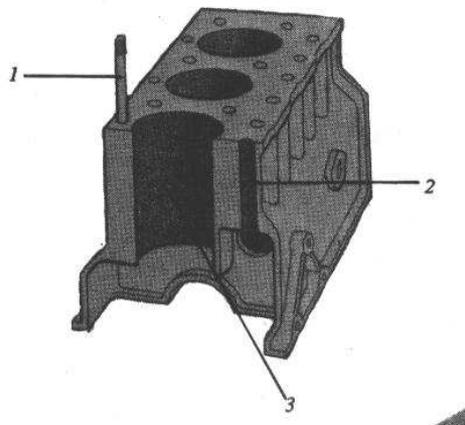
Vista em corte de um bloco com camisas usinadas nele próprio. (1- Estojo de fixação 2- Abertura para hastes de válvulas 3- Cilindro de corte)
